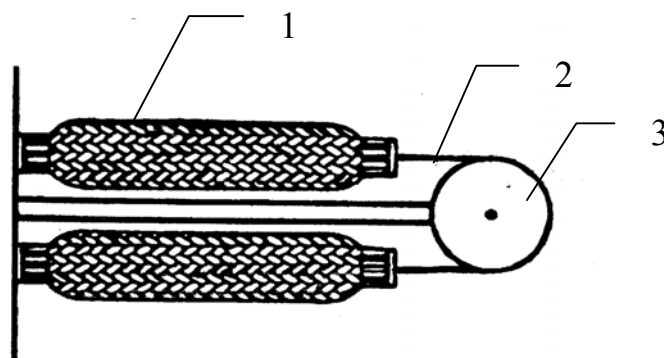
Реверсивный гибкий пневматический привод фирмы «Бриджестоун»:
